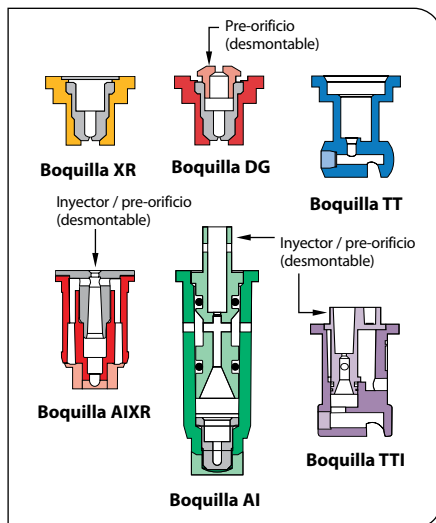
Boquillas XR, DG, TT, TTJ60, AIXR, AI y TTI (vista transversal).
